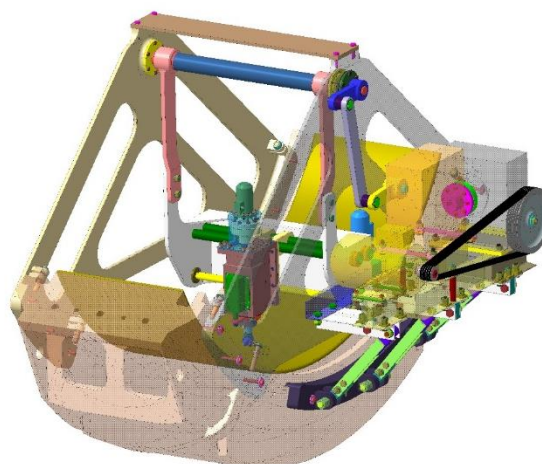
Общий вид специального станочного модуля для обработки крупногабаритных подшипников
